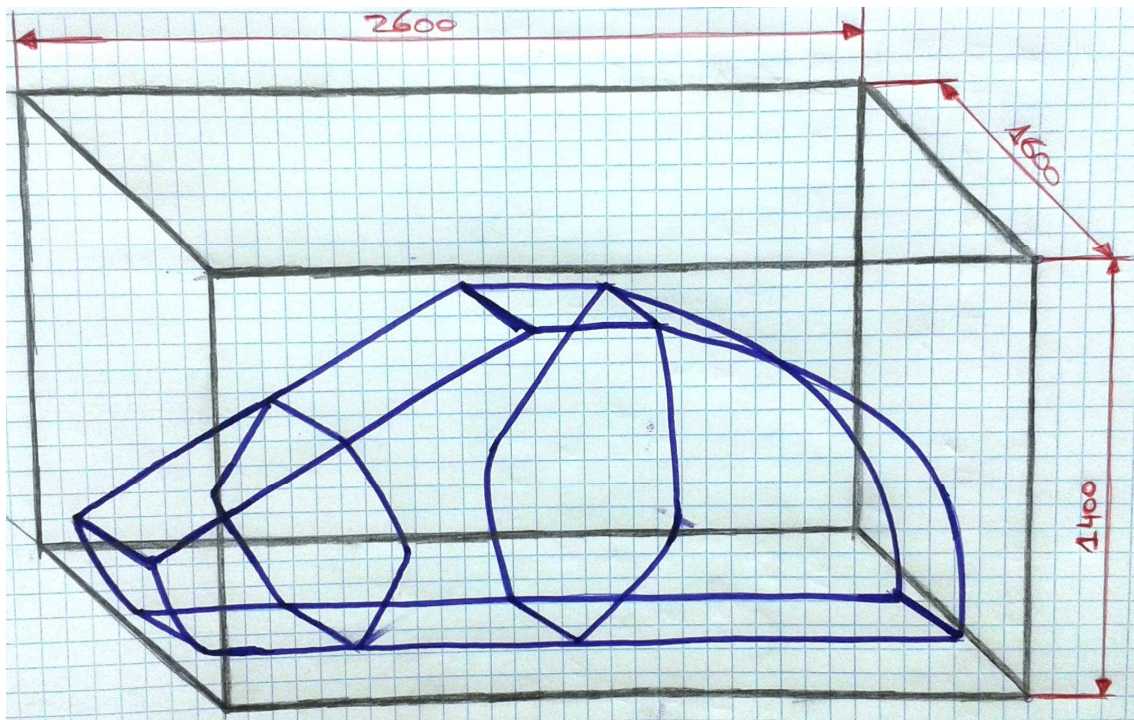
Boceto de la estructura principal a mano alzada. Fuente: elaboración propia.
